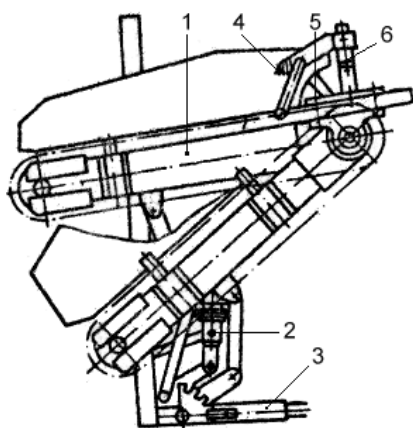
Регулировка расположения основной и дополнительной горок:
